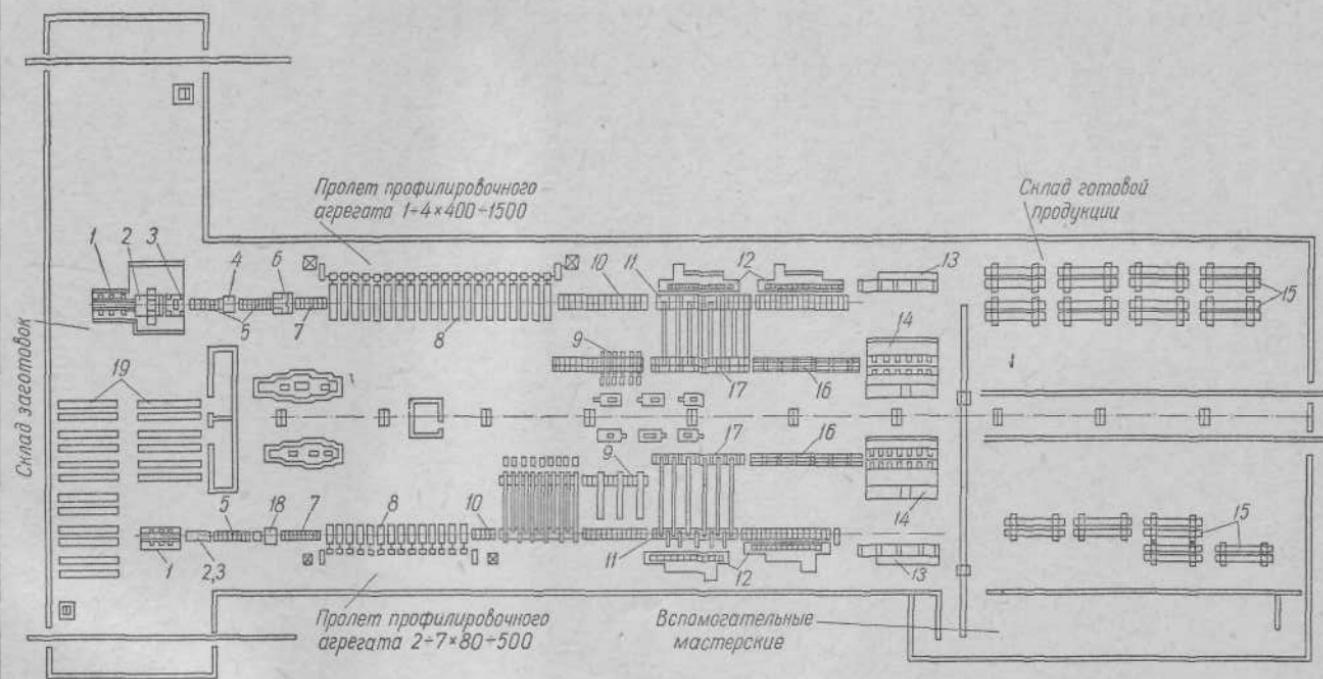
Расположение оборудования профилегибочных агрегатов 2-7×80-500 и 1-4×400-1500:
